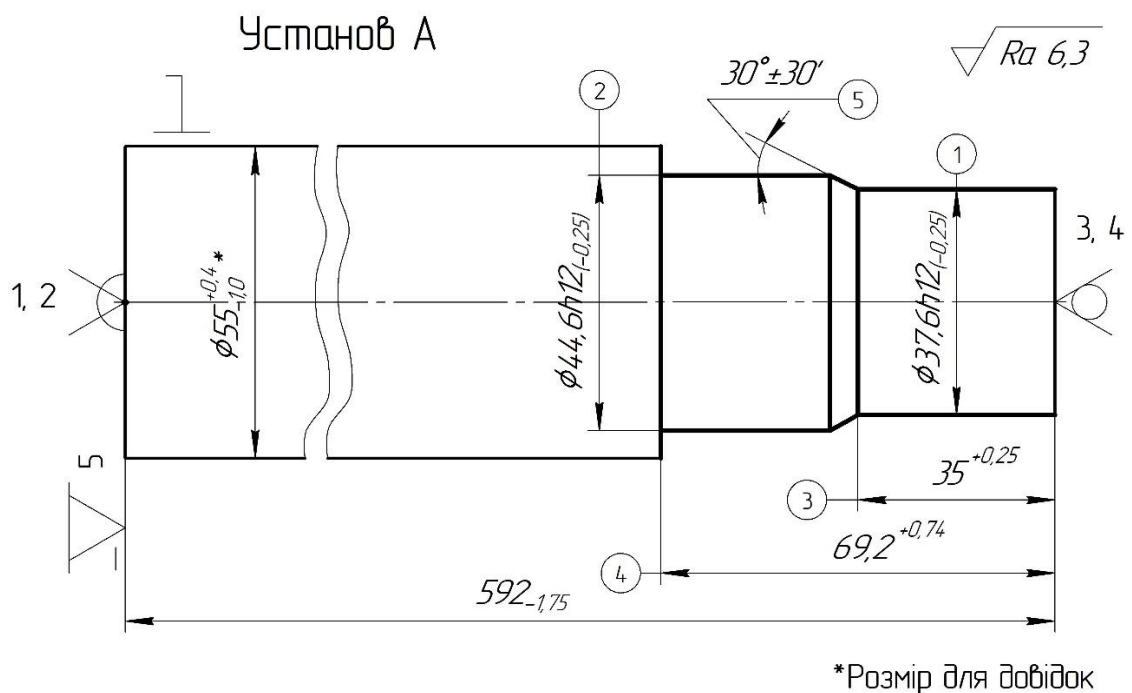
Ескіз заготовки на операції 015. Установ А
